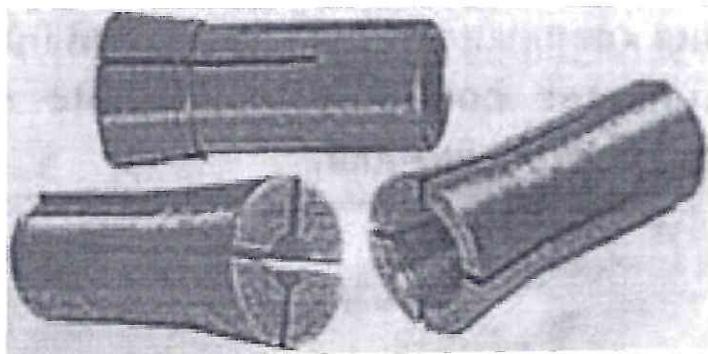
Конструкция шпильковертов с разрезными втулками
